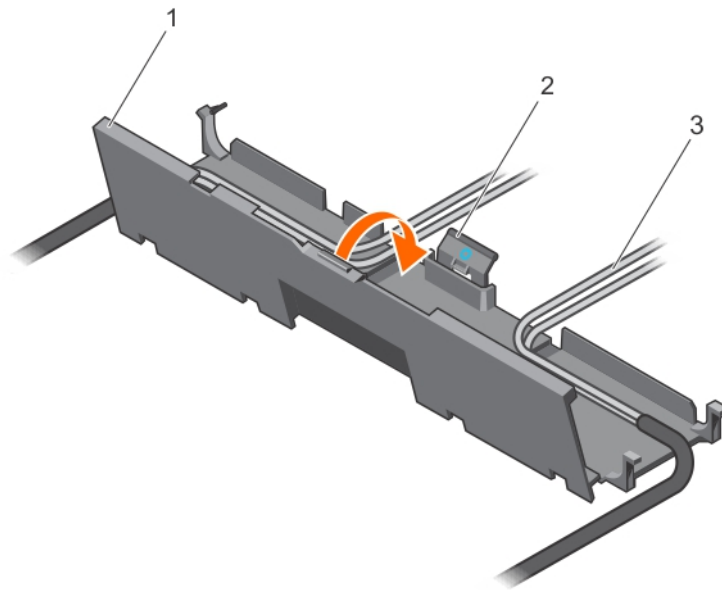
Colocación de los cables por la bandeja para tendido de cables
